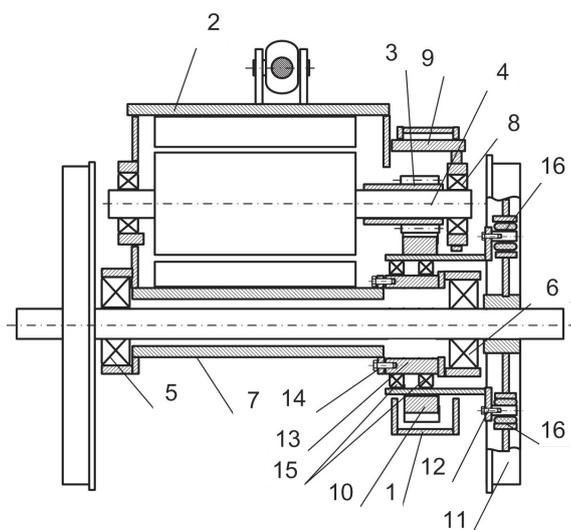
Опорно-осевой привод с упругими элементами, расположенными на диске колеса: 1 – редуктор; 2 – ТЭД; 3 – малое зубчатое колесо; 4 – вал ТЭД; 5, 6 – МОП качения; 7 – корпус; 8 – роторный подшипник; 9 – защитный корпус; 10 – большое зубчатое колесо; 11 – колесо колесной пары; 12, 14 – болты; 13 – стакан; 15 – подшипники; 16 – амортизаторы
